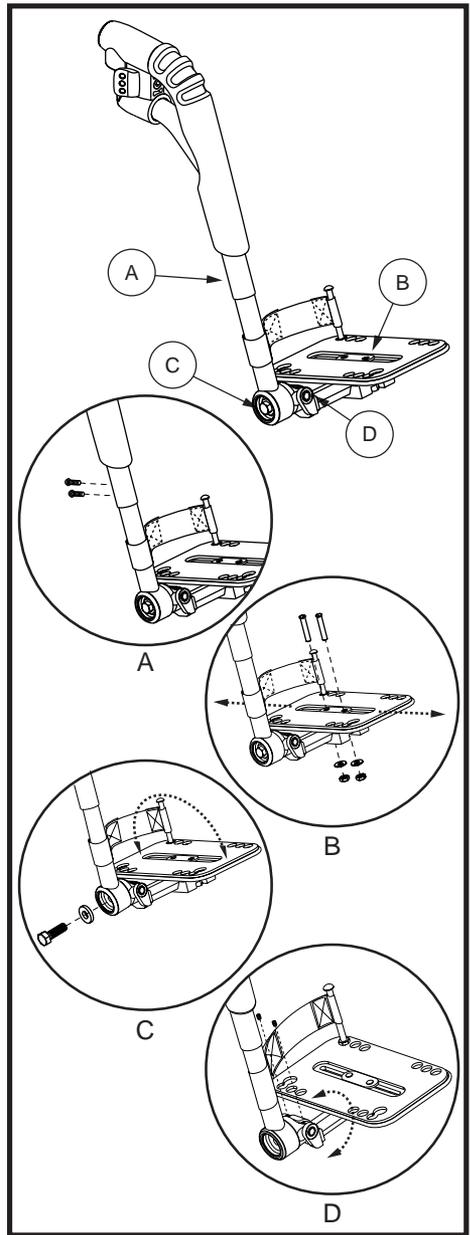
Mehrachsen-Fußplatte für ausschwenkbare Fußstütze der Ausführung Nr. 8
